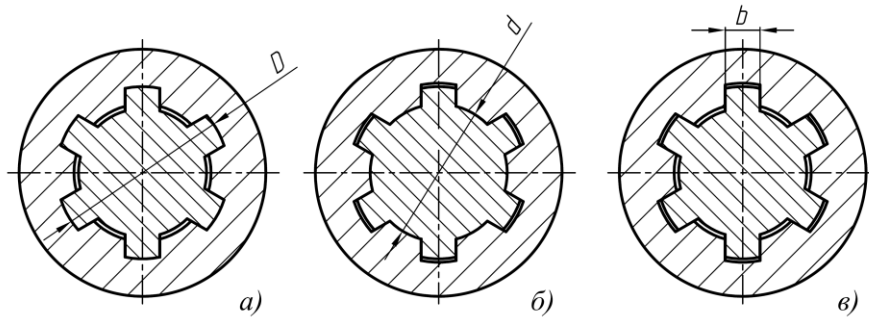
Способи центрування шліцьових з'єднань:
